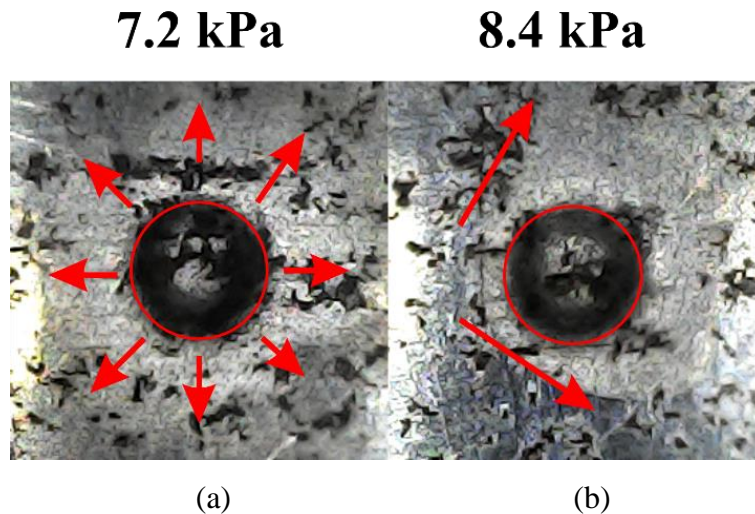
Efecto abanico presente en maquinados al aplicar un flujo de aire a una presión igual o mayor a 8.4 kPa
